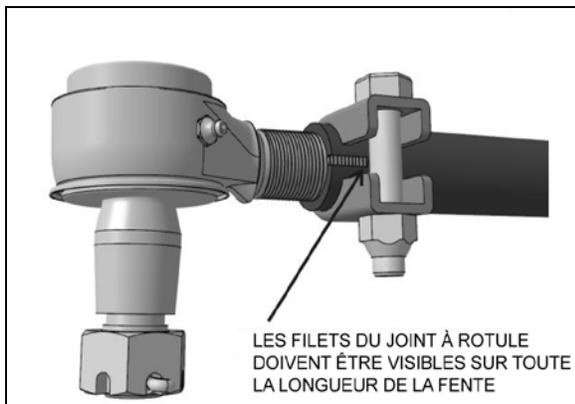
CONDITIONS D'UN SERRAGE CORRECT
